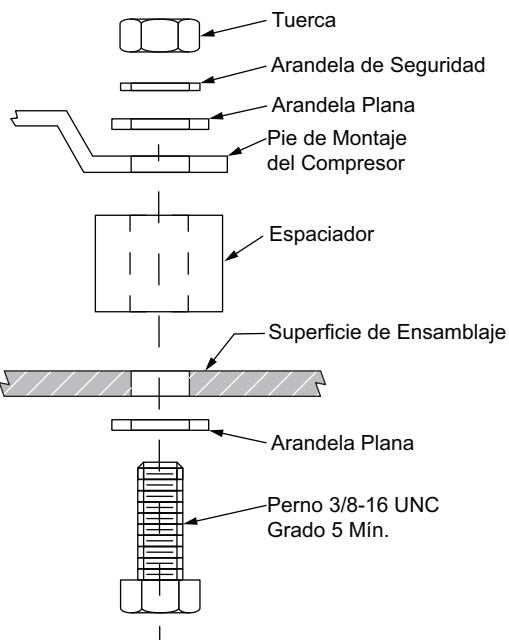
Montaje rígido (pie de placa con espaciador)
